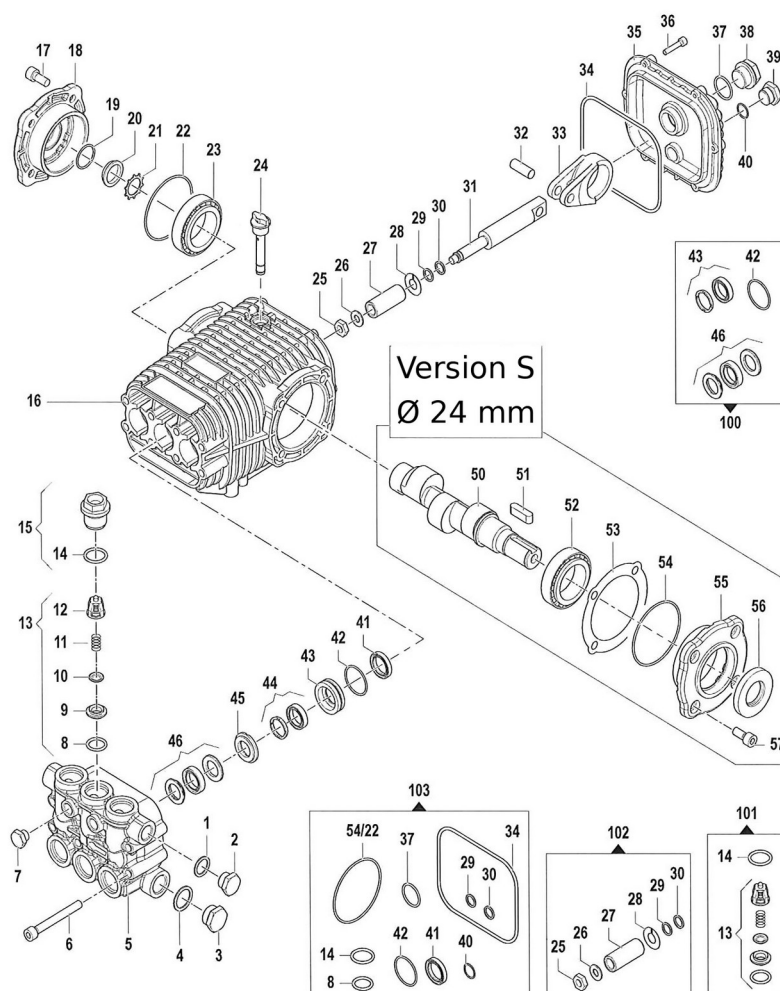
Vue éclatée de la pompe COMET RW PF
